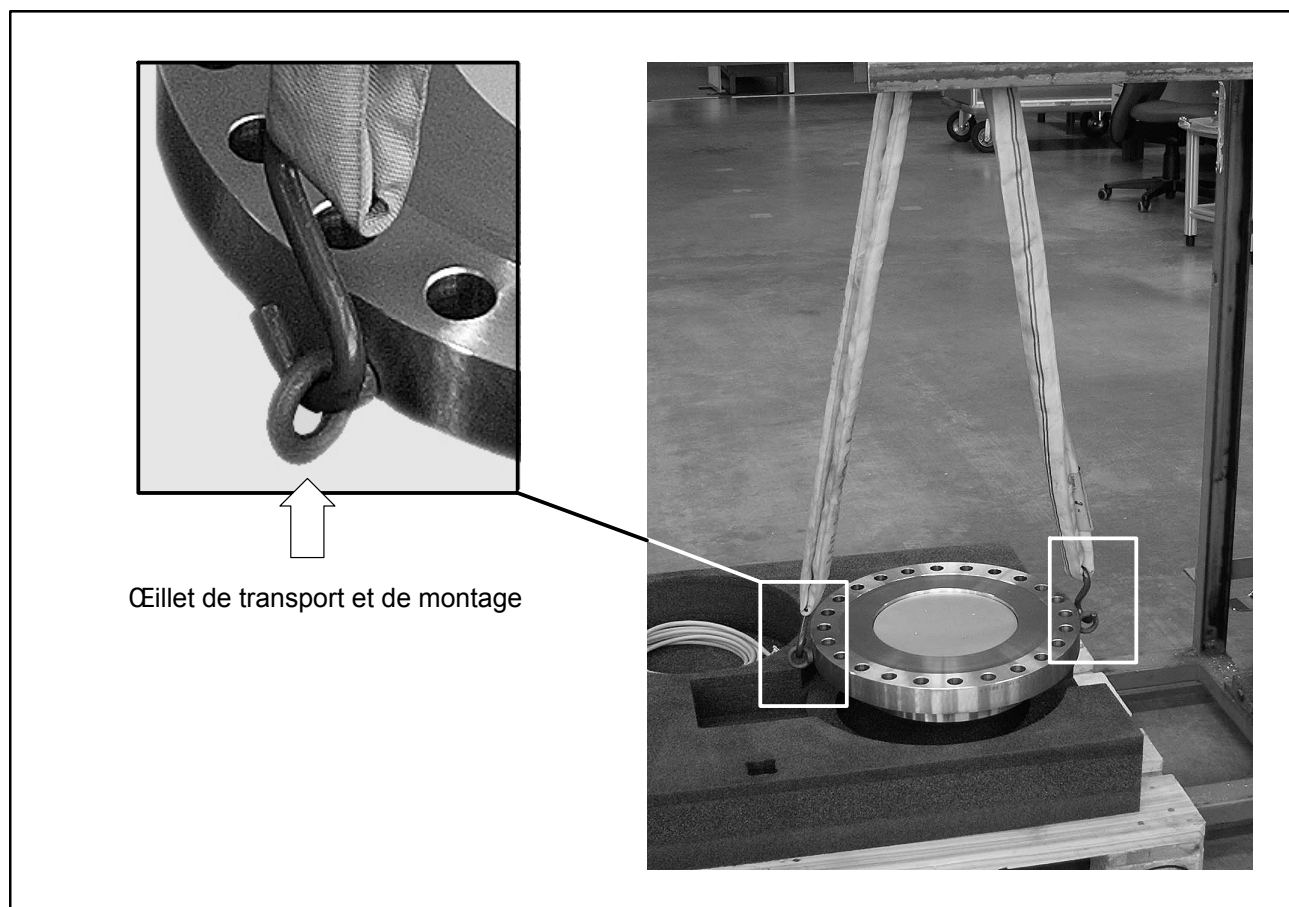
Œillets sur le rotor pour le transport et le montage
